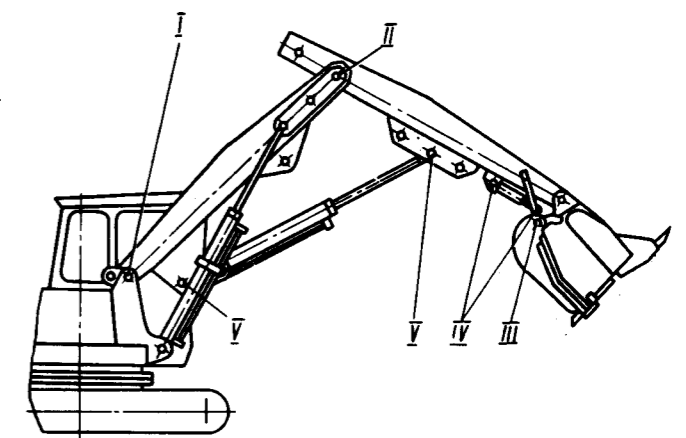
Схема смазки рабочего оборудования прямая лопата
